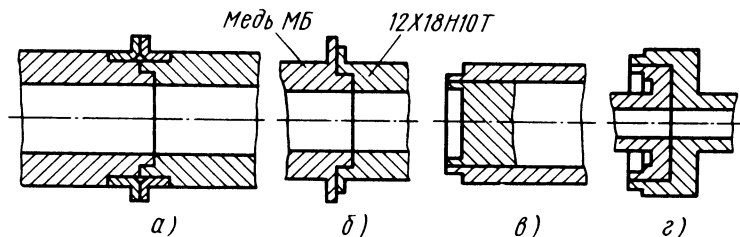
Соединения, получаемые аргонодуговой сваркой в камере:
